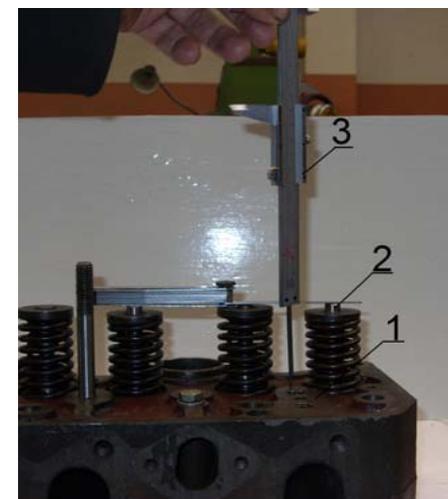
Измерение расстояния между верхней обработанной поверхностью головки цилиндров и торцом стержня клапана: 1 – верхняя обработанная поверхность головки цилиндров; 2 – торец стержня клапана; 3 – штангенглубиномер ШГ-160
